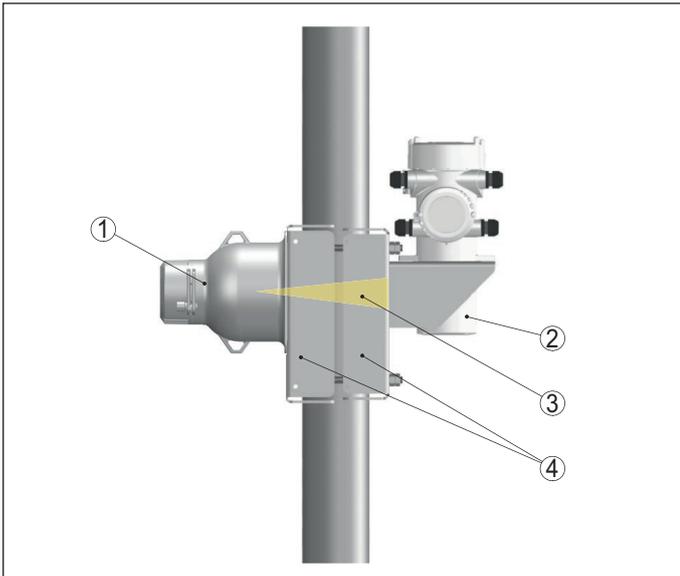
Dispositivo di fissaggio per il montaggio su tubi da 50 ... 220 mm (1.97 ... 8.66 in) con inclinazione di irraggiamento di 30°
